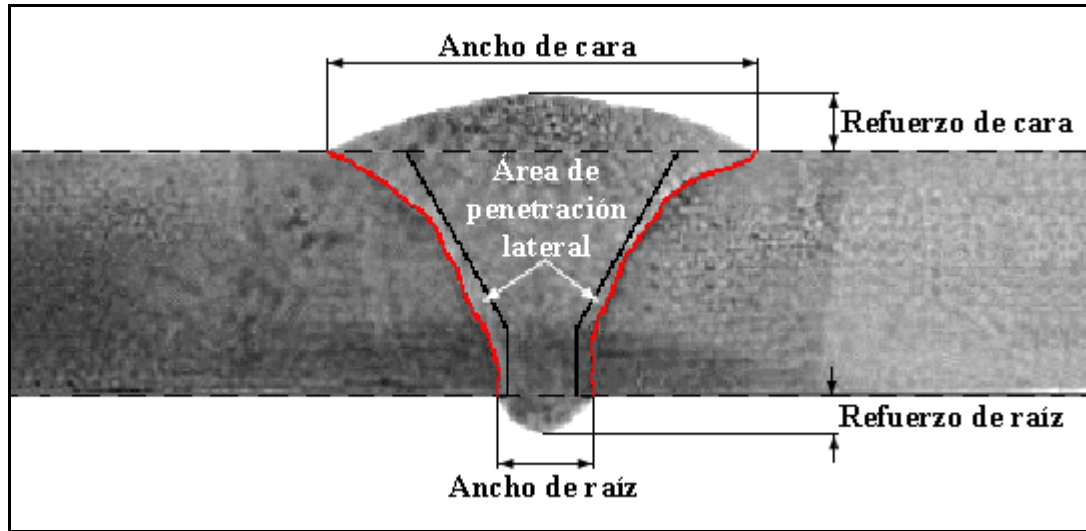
Parámetros geométricos del cordón de soldadura.
